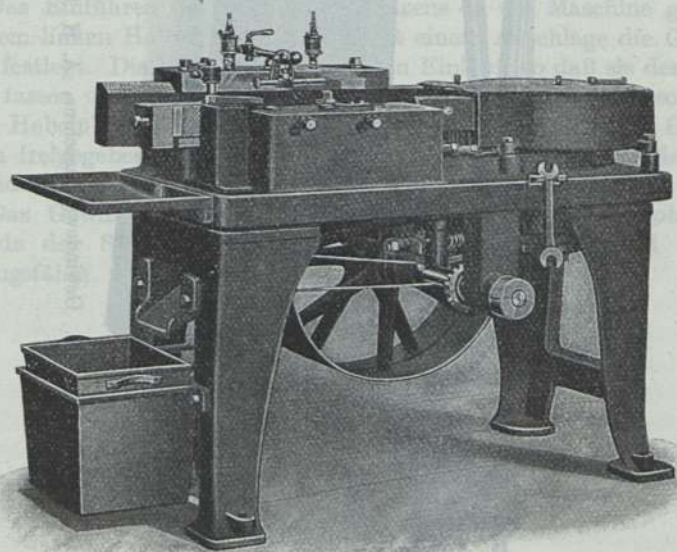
Gewinderollmaschine. A. H. Schütte, Köln-Deutz.
